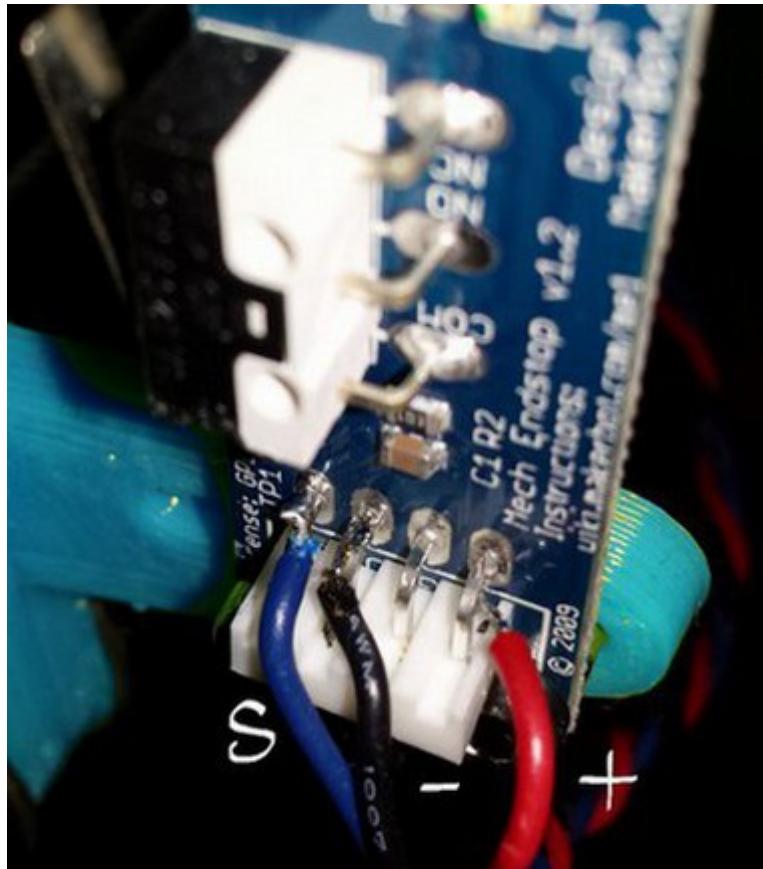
soudure sur endstop monté sur carte makerbot
